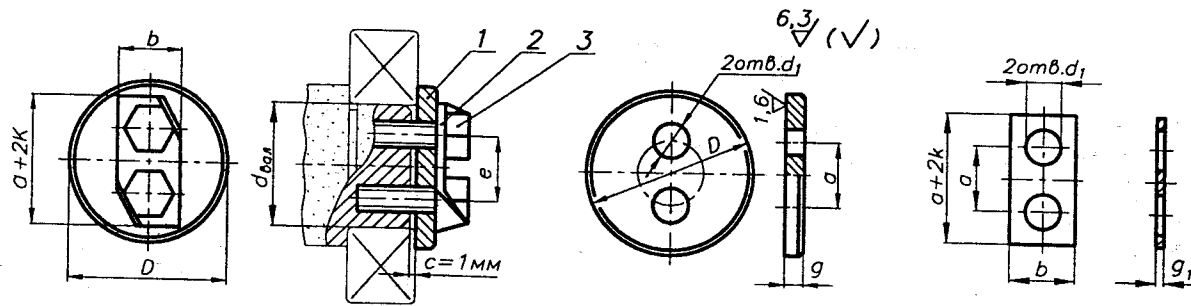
Закрепление подшипника на валу с использованием концевой шайбы:
